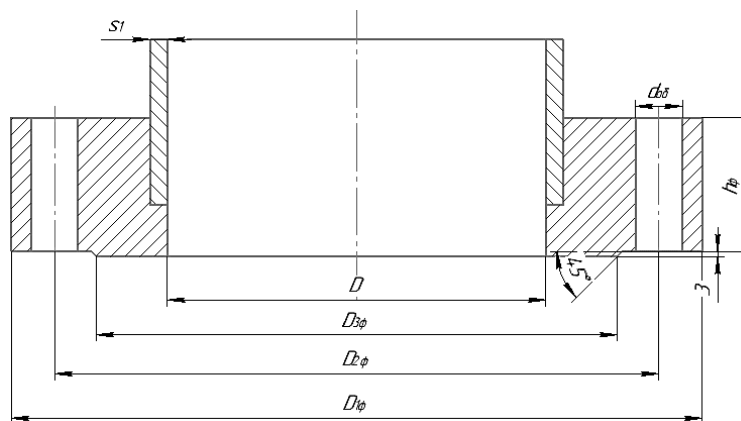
Размеры плоского приварного фланца с гладкой уплотнительной поверхностью
